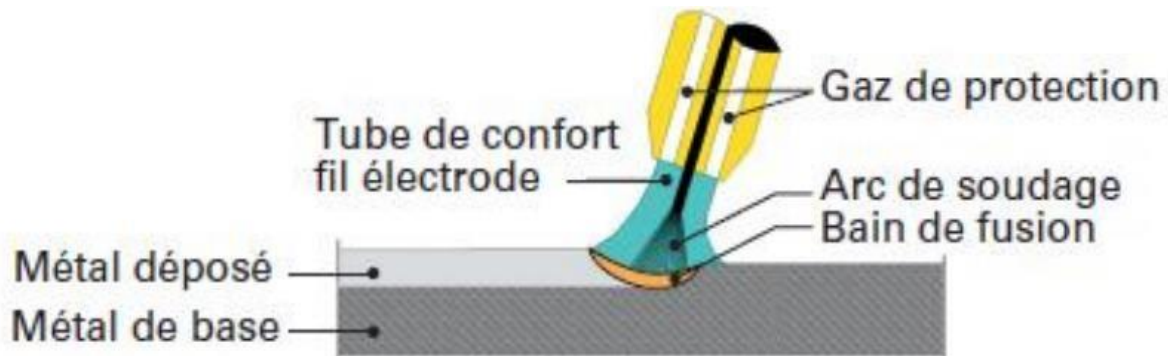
SOUDAGE SOUS FLUX GAZEUX [6]
